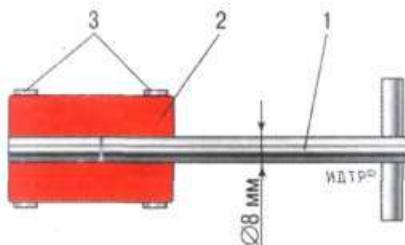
Приспособление для притирки клапанов: 1 – металлический стержень; 2 – резиновый шланг; 3 – винтовой хомут
